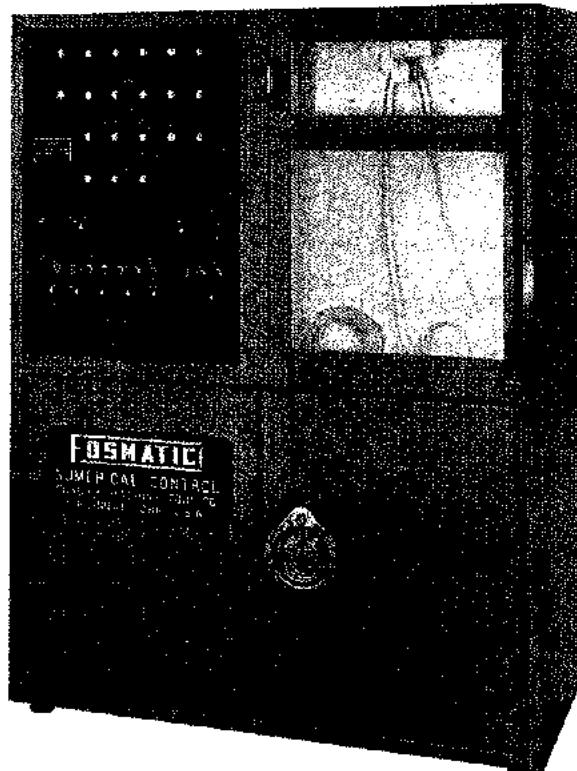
Lector de cinta para una máquina herramienta controlada numéricamente (Fosdick Machine Tool Co.)
